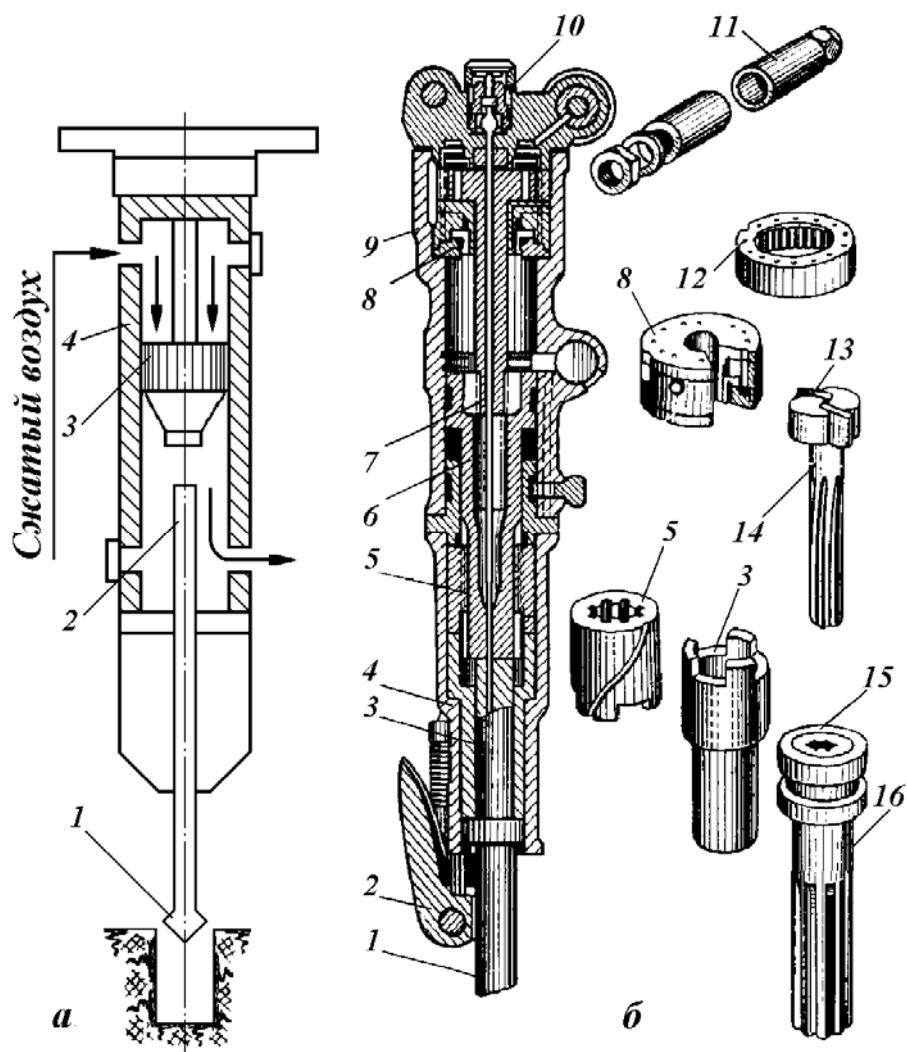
Схема устройства пневматического перфоратора: а – схема; б – конструкция перфоратора: 1 – бур; 2 – буродержатель; 3 – поворотная муфта; 4 – корпус поворотного механизма; 5 – ведущая муфта; 6 – направляющая букса; 7 – геликоидальный стержень; 8 – воздухораспределительное устройство; 9 – корпус; 10 – промывочное устройство; 11 – ручки; 12 – храповое кольцо; 13 – собачка; 14 – головка; 15 – геликоидальная гайка; 16 – шток поршня
